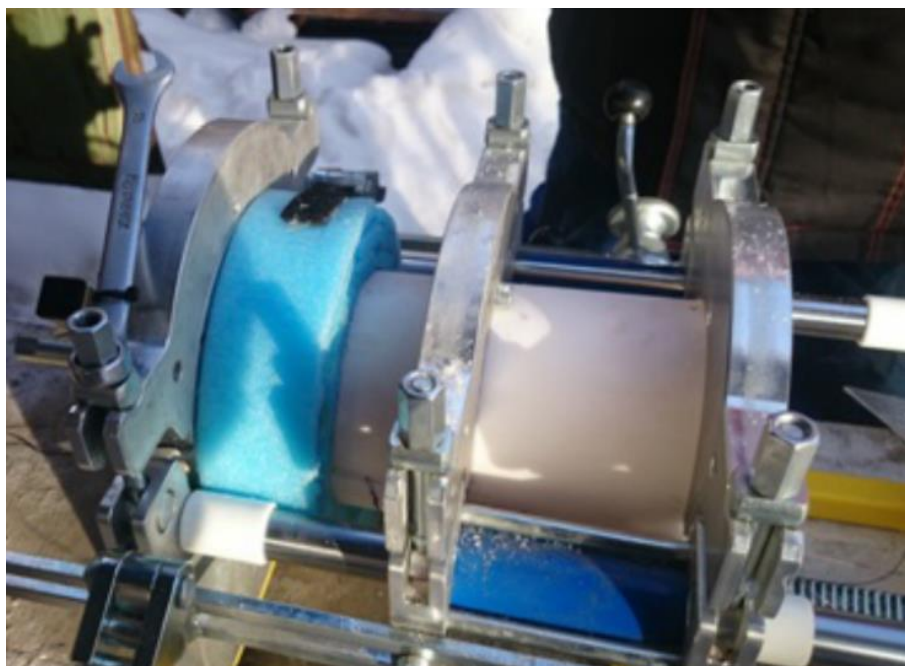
Охлаждение сварного раструбного соединения под слоем теплоизоляции после сварки
